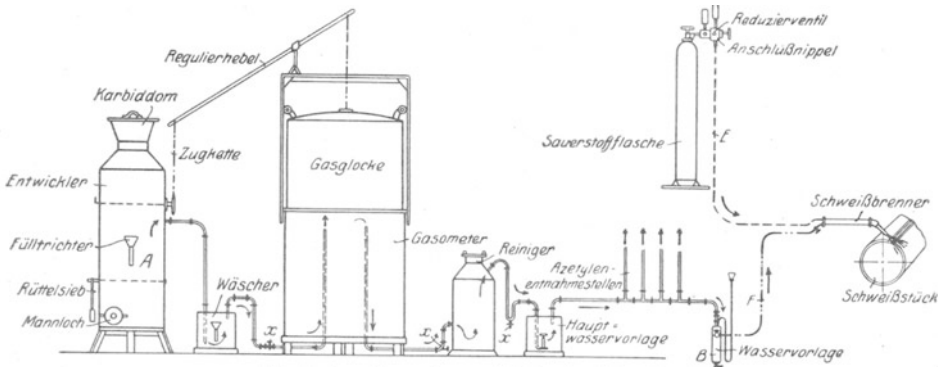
Grundform einer ortsfesten Azetylenschweißanlage.
